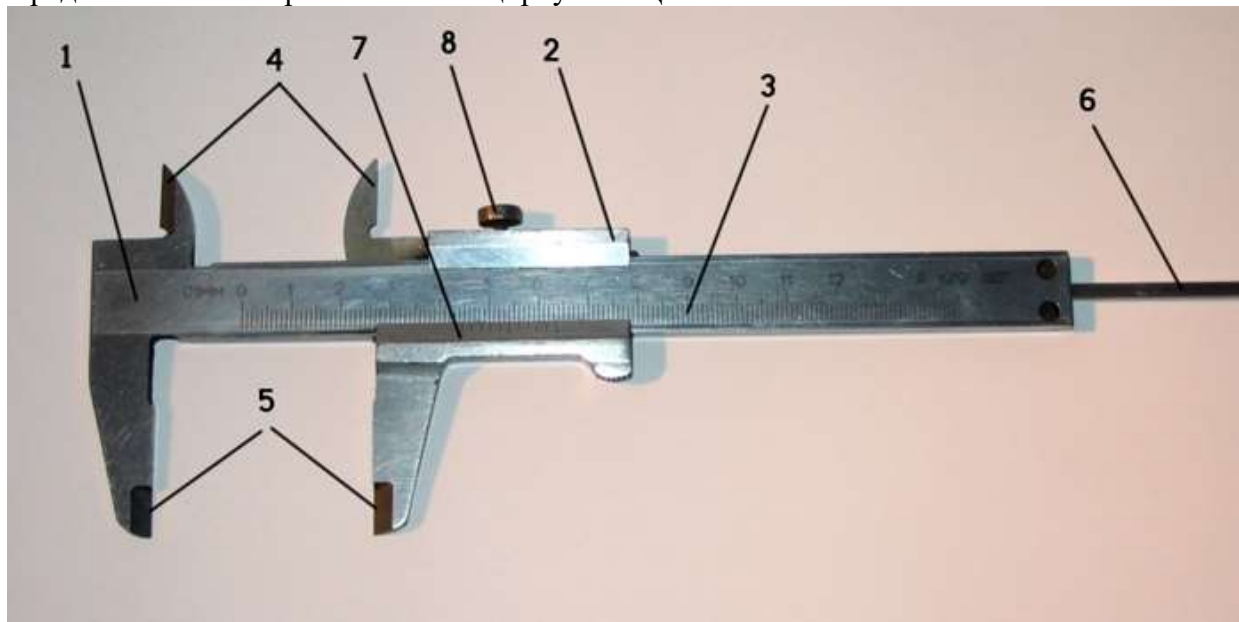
Штангенциркуль типа ШЦ-1: 1 - штанга; 2 – рамка; 3 - измерительная шкала; 4 - верхние губки; 5 - нижние губки; 6 – глубиномер; 7 - шкала нониуса; 8 - зажимной винт
